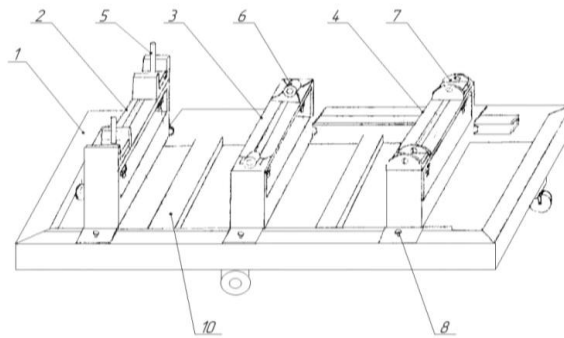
Универсальный стенд-кондуктор для разборки (сборки) кузовов автомобилей
